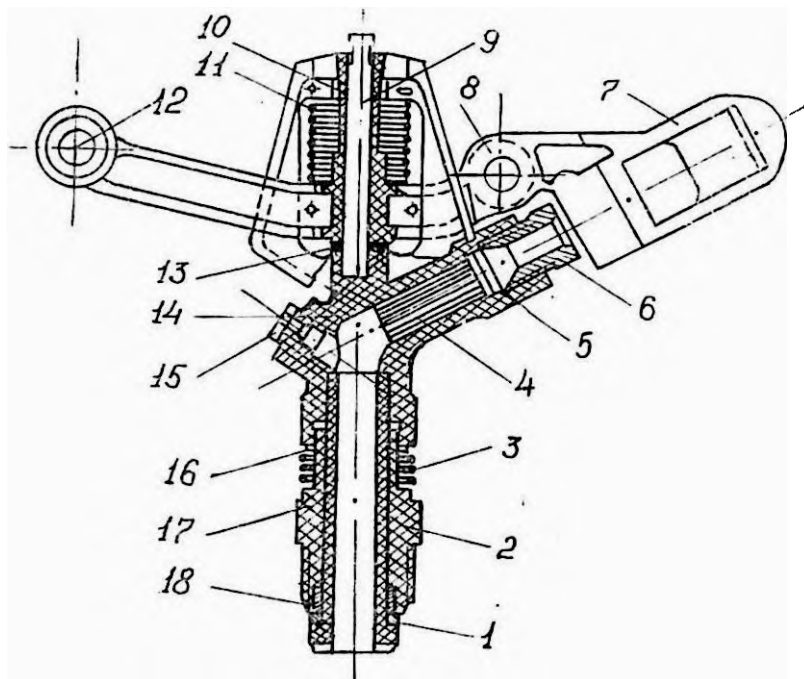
Дождевальный аппарат типа АД-1: 1 — шайба; 2 — штуцер; 3, 11 — пружины; 4 — стабилизатор; 5 — ствол; 6 — сопло; 7 — коромысло; 8, 12 — вставки; 9 — ось; 10 — колпак; 13 — резиновое кольцо; 14 — корпус; 15 — пробка; 16 — корпус-кольцо; 17 — втулка; 18 — гнанд-букса.
